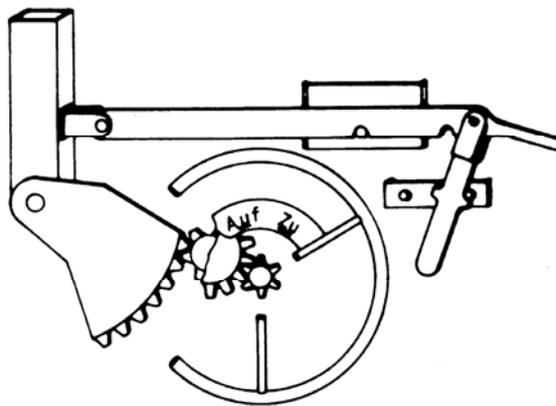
„Grundstellung“; das Schwenkdach ist verriegelt und geschlossen.
